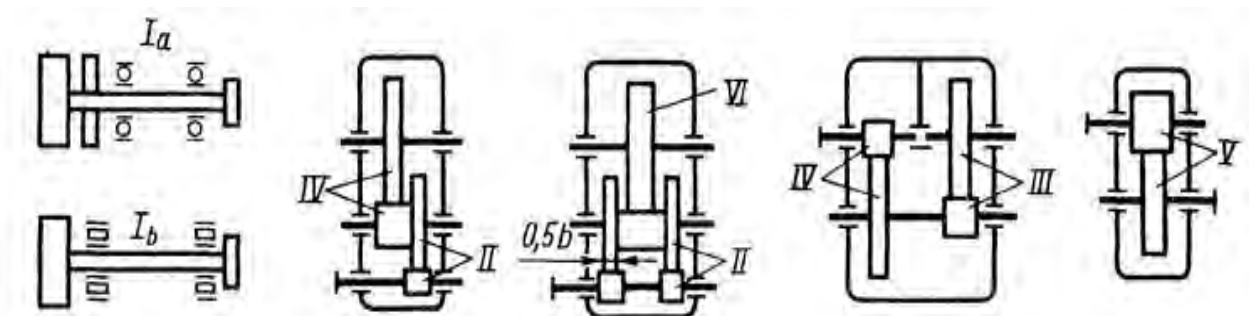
Виды расположения шестерни и колеса в редукторе
